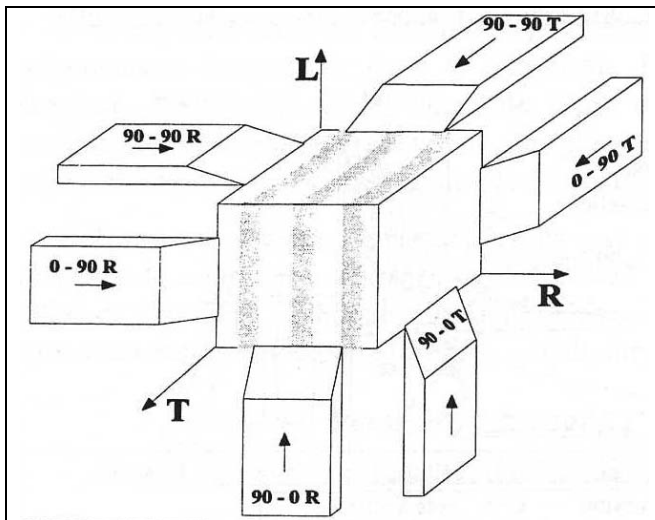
Modes de coupes fondamentaux, en coupe orthogonale du bois d'après [MCK61]
